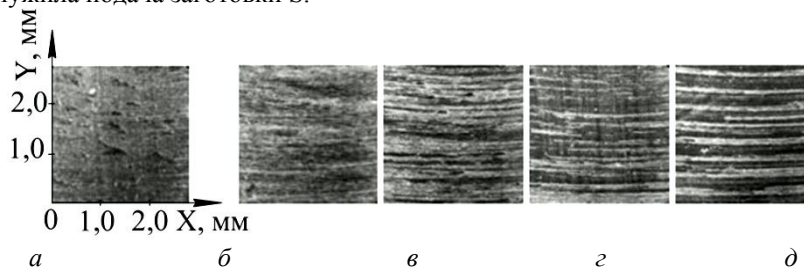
Мікрофотографії поверхонь пластин із сталі 35 після торцевого фрезерування ($n = 125$ об/хв, $t = 1$ мм) з різними значеннями подачі S :
